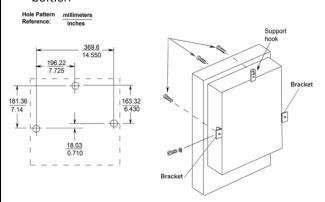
Montage sur une surface, panneau ou mur (vue arrière)
